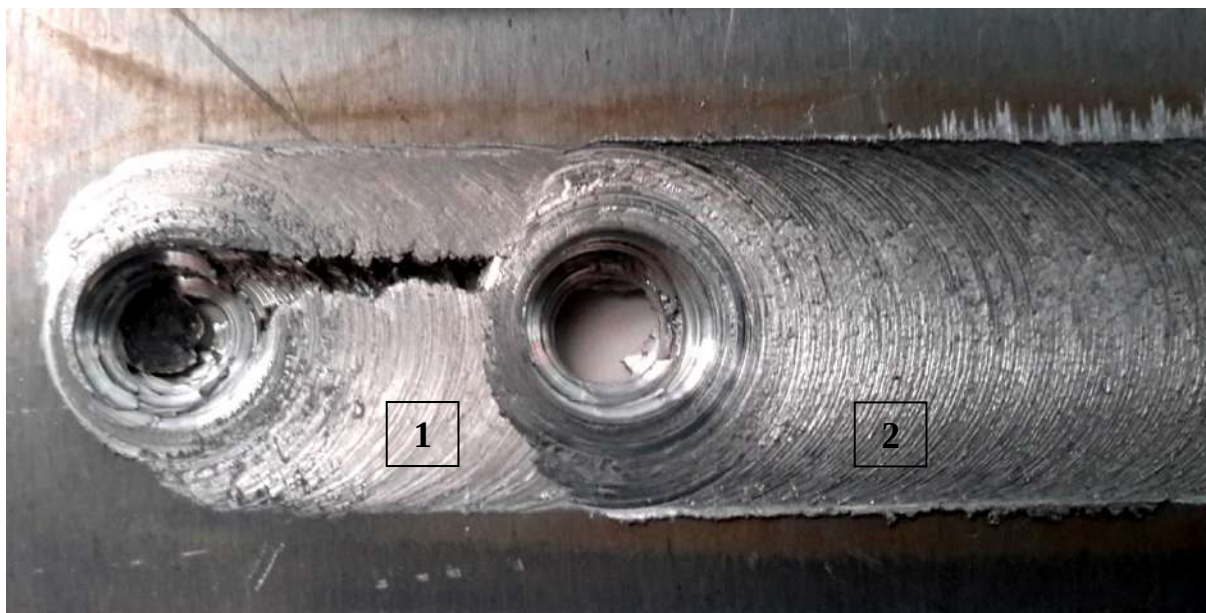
Подварка вторым проходом дефектов типа несплавления, дефект типа wormhole и несплавления в корневой части шва:
